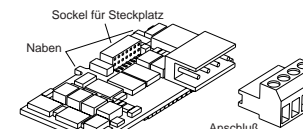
Entfernen Sie den Steckverbinder, bevor Sie das Eingang-1-Modul installieren.
